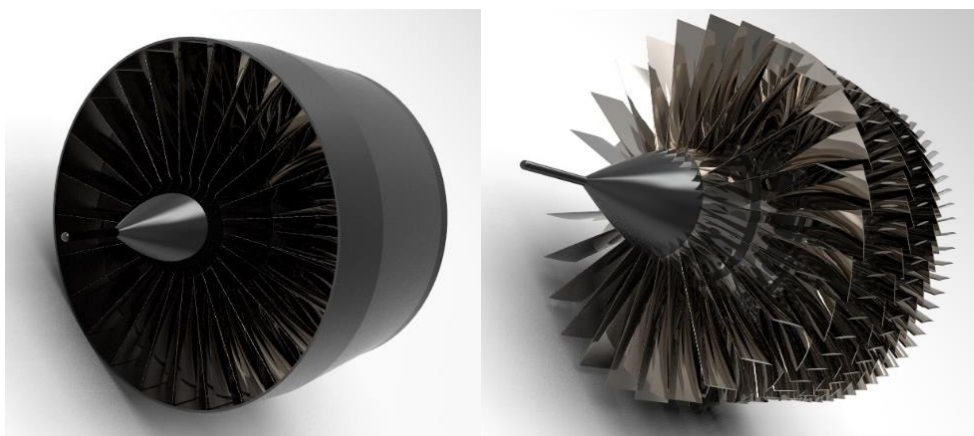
Geometria wieńców kierowniczych a) i wieńców wirnikowych b) w złożeniu
